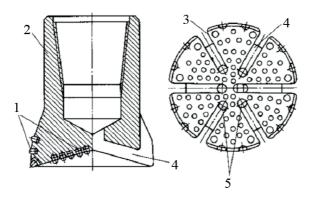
Торцовое долото: 1 – твердосплавные штыри; 2 – цилиндрический корпус; 3 – боковые пазы; 4 – радиальные канавки; 5 – промывочные каналы
